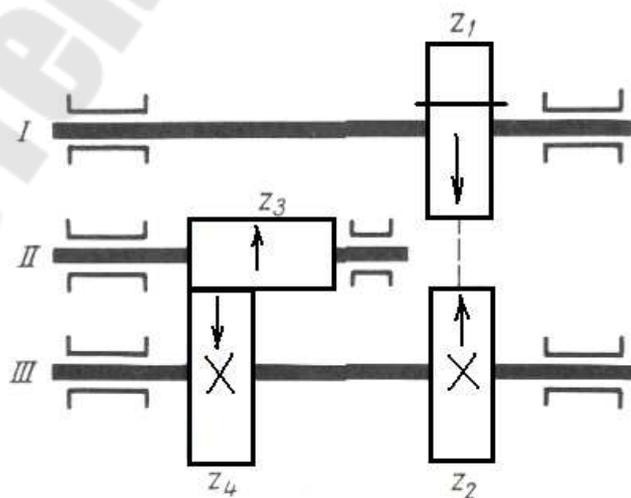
Схема реверса с составным зубчатым колесом
